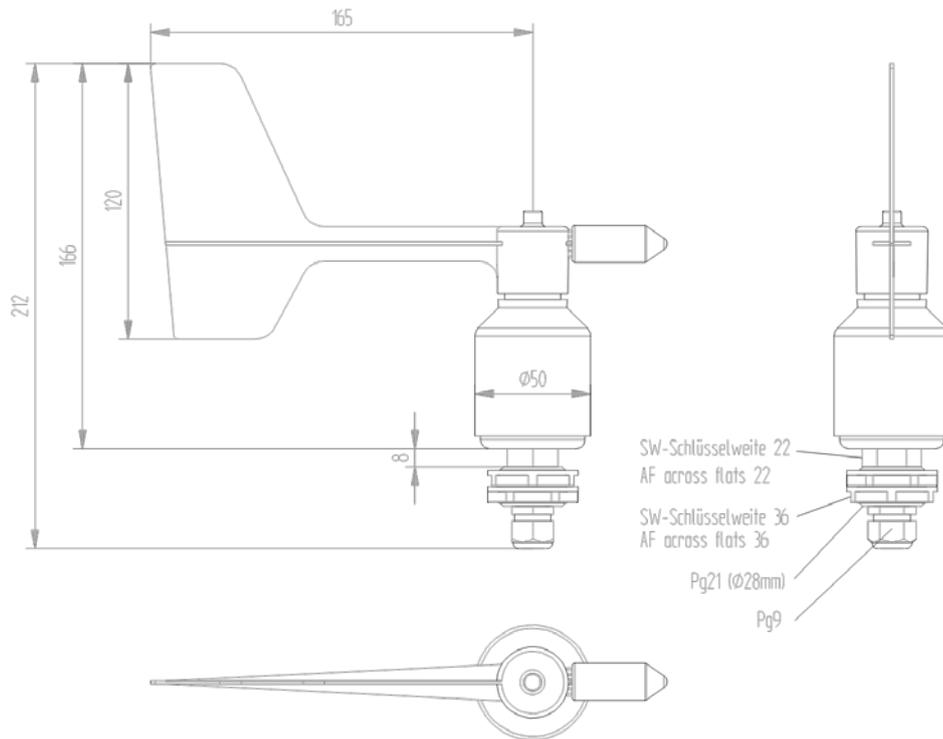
Maßbild für Ausführung mit Kabelverschraubung
